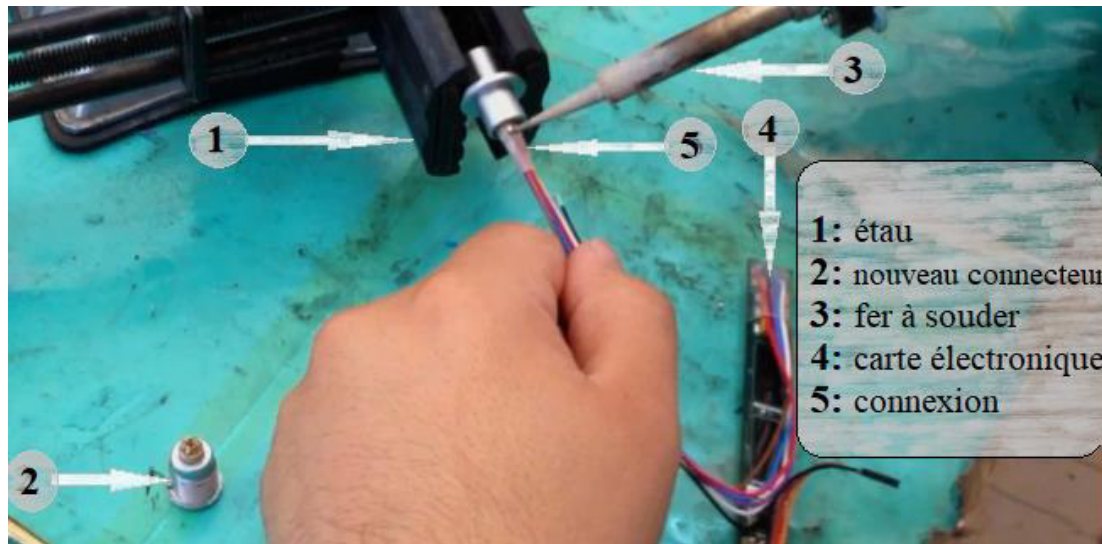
Dessoudage et soudage du connecteur de batterie
